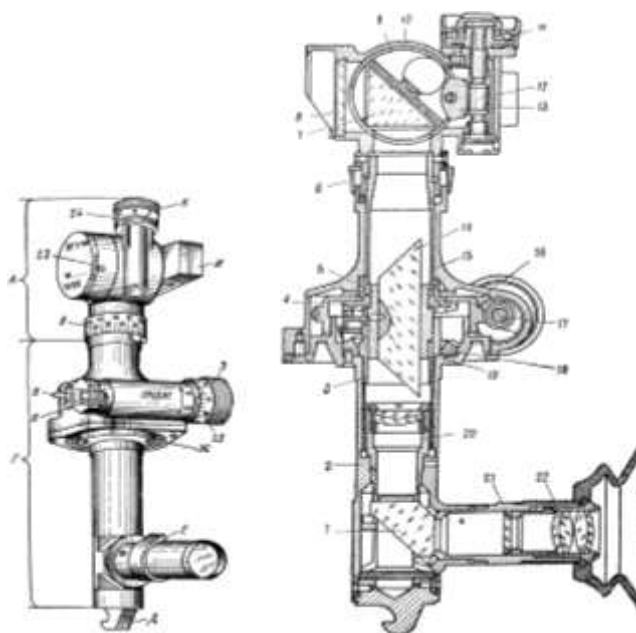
Артилерійська панорама ПГ-1М: А – поворотна частина панорами; Б – відведення черв'яка; В – гальмо; Г – нерухомий корпус; Д – гак; Е – окуляр; Ж – конічний паз; З – механізм кутоміра; І – візирний пристрій; К – механізм відбивача; 1 – призма АКР-90°; 2 – корпус; 3 – напрямний циліндр; 4 – проміжна шестерня; 5 – верхня шестерня; 6 – шкала грубого відліку кутоміра; 7 – призма АР-90°; 8 – захисне скло; 9 – обойма відбивача; 10 – поворотна головка; 11 – маховик відбивача; 12 – черв'як; 13 – черв'ячний сектор; 14 – призма АР-0°; 15 – корпус кутоміра; 16 – черв'ячне колесо; 17 – черв'як кутоміра; 18 – нерухома шестерня; 19 – обойма; 20 – об'єктив; 21 – пластина з сіткою панорами; 22 – окуляр; 23 – шкала грубого відліку відбивача; 24 – маховик відбивача зі шкалою точного відліку; 25 – маховик кутоміра зі шкалою точного відліку
